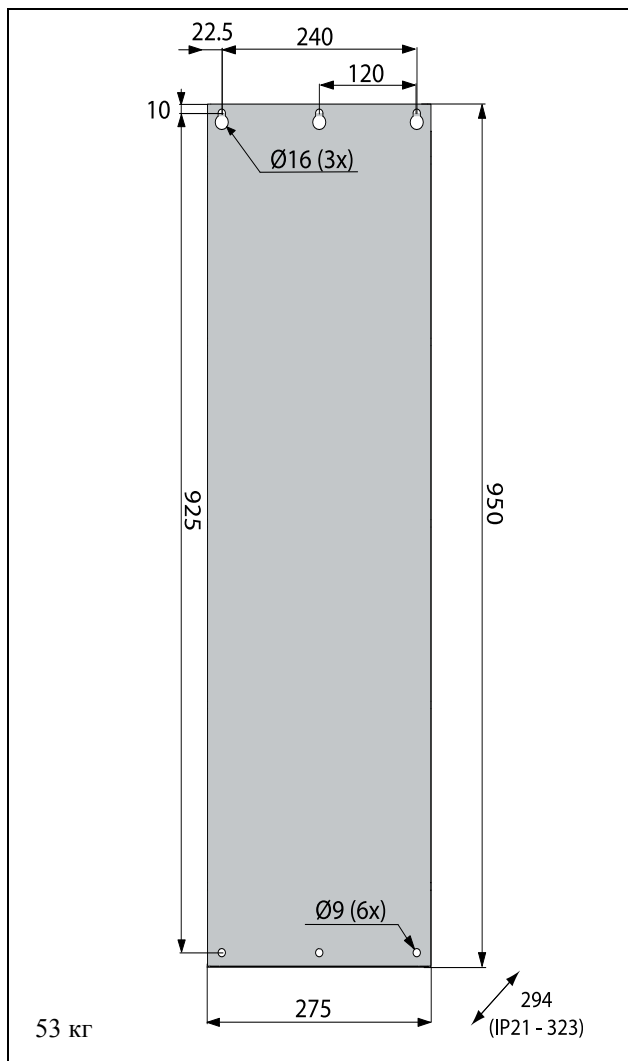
Устройство Etotron /FDU моделей 48-106 – 48-171 (типоразмер корпуса E2).
